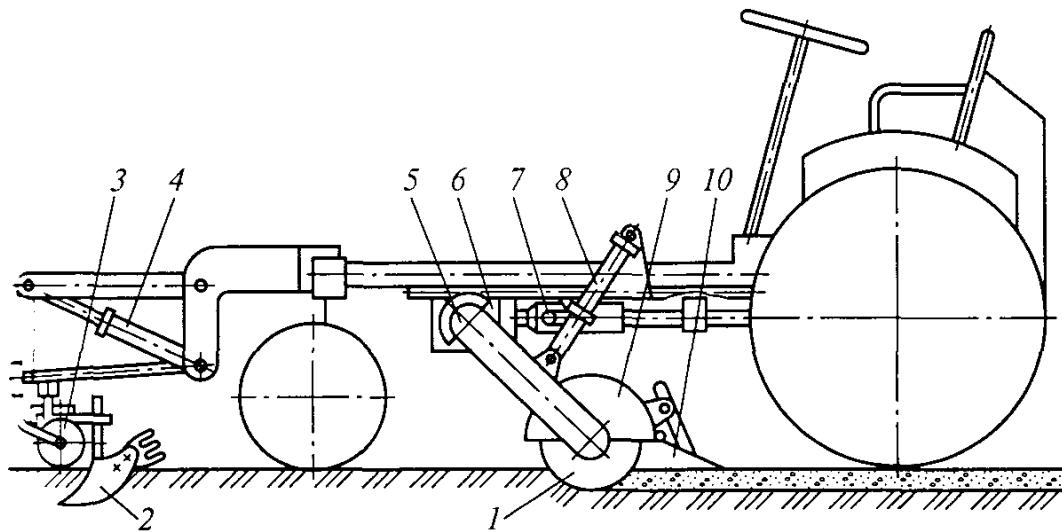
Фреза ґрунтовая ФПШ-1,3: 1 – фрезерний барабан; 2 – грядокоутворюючий корпус; 3 – опорне колесо, 4 – виносний гідроциліндр; 5 – ланцюгова передача; 6 – редуктор, 7 – карданна передача; 8 – гідроциліндр; 9 – захисний кожух ; 10 – планувальник
